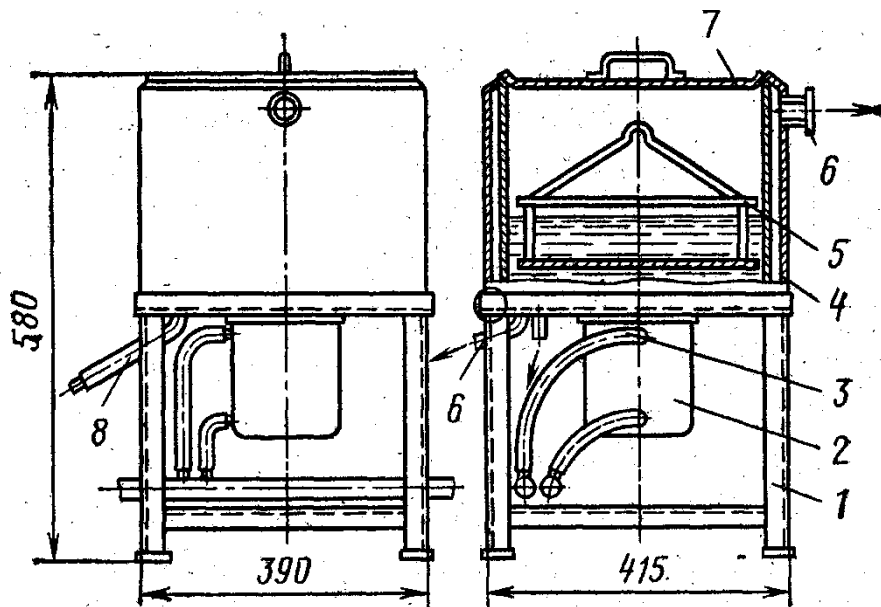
Універсальна ультразвукова ванна: 1 – каркас; 2 – перетворювач; 3 – патрубок; 4 – корпус ванни; 5 – кошик; 6 – патрубок; 7 – кришка; 8 – патрубок
